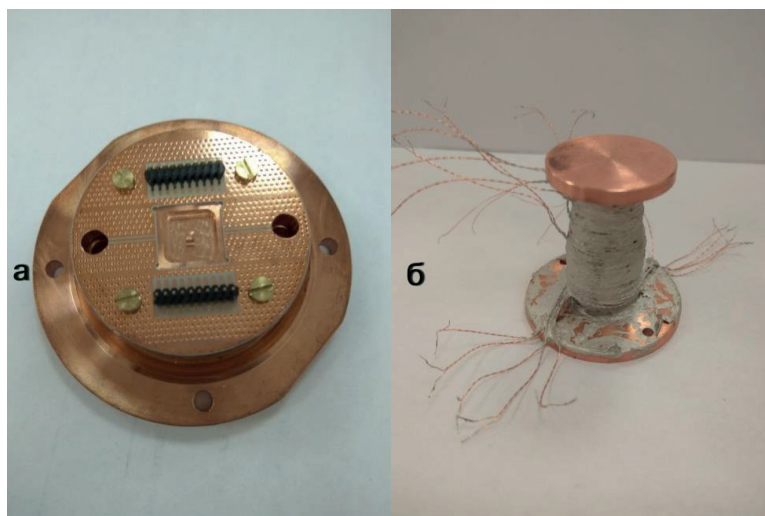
Изготовленные а – крышка в сборе с платой для образцов, б – фильтрационный блок для 10 витых пар
